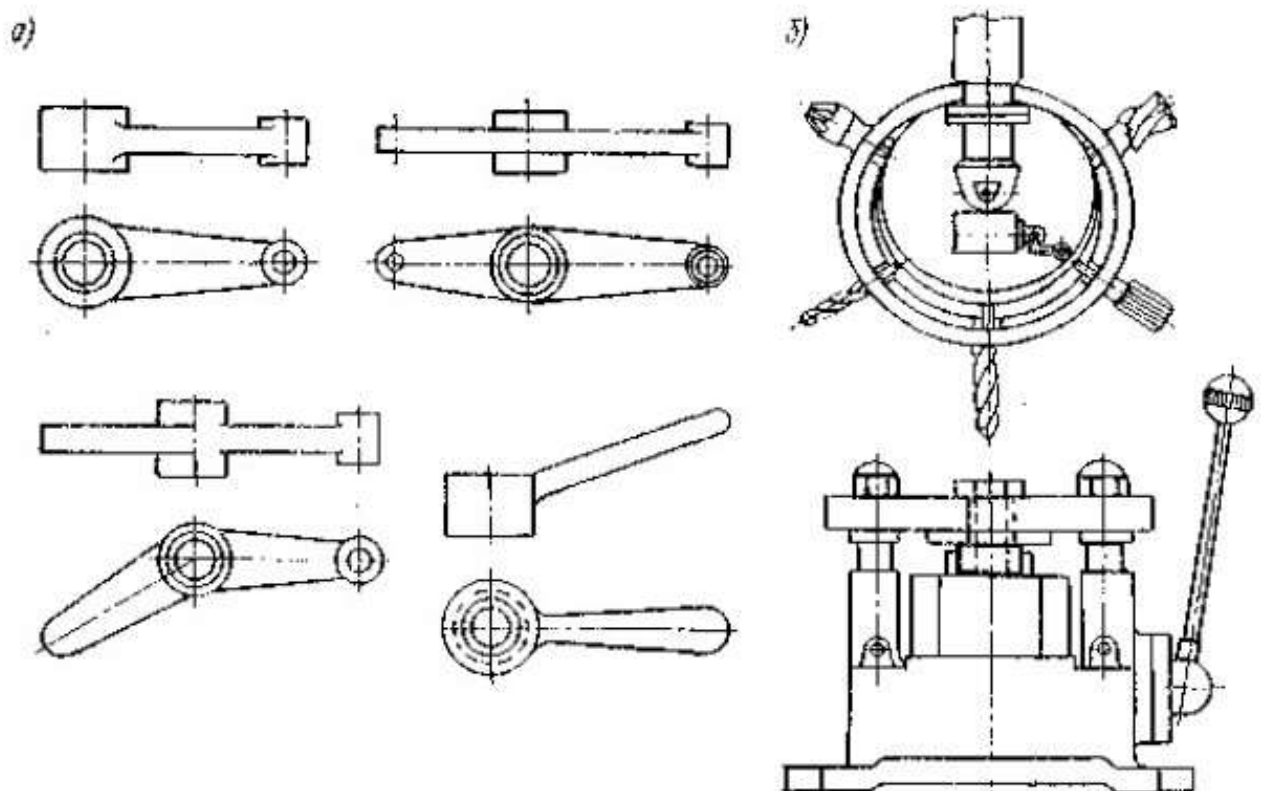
Група деталей й групова оснастка свердлильного верстату.
